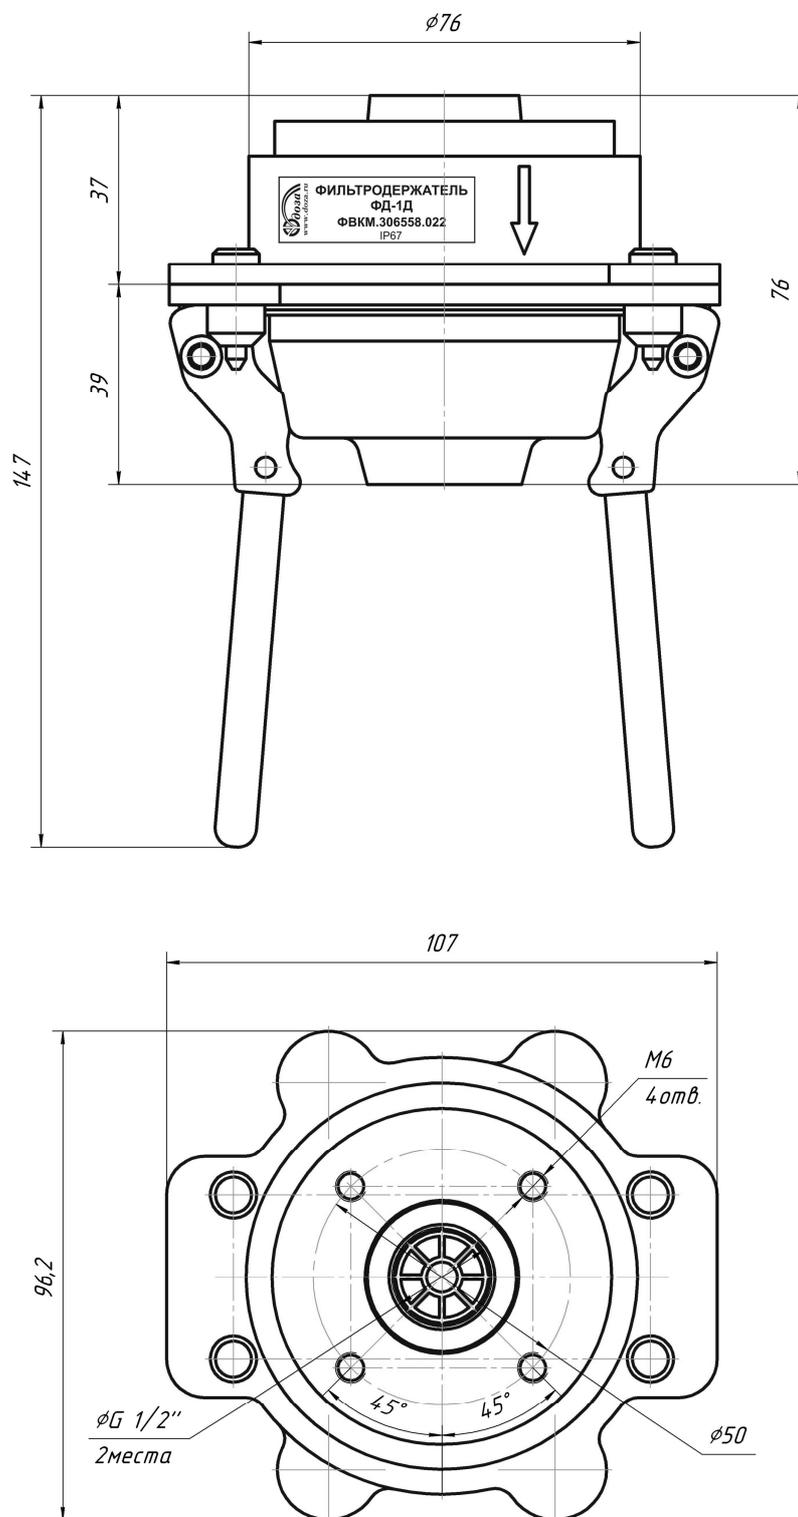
Габаритные и присоединительные размеры фильтродержателя
